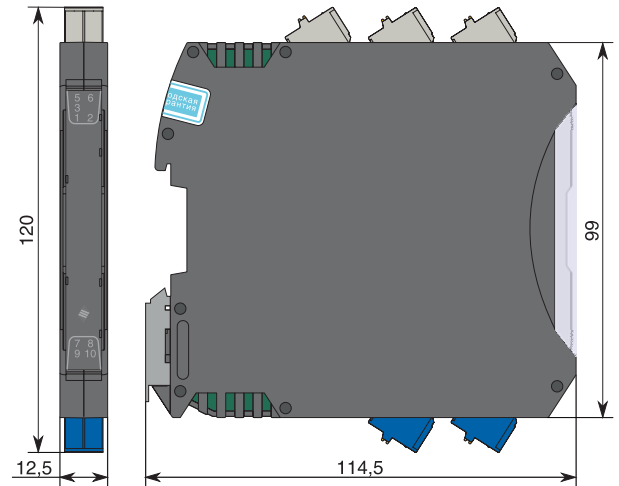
Габаритные размеры барьера в корпусе шириной 12,5 мм с разъемами с пружинными клемниками и тестовыми гнездами
